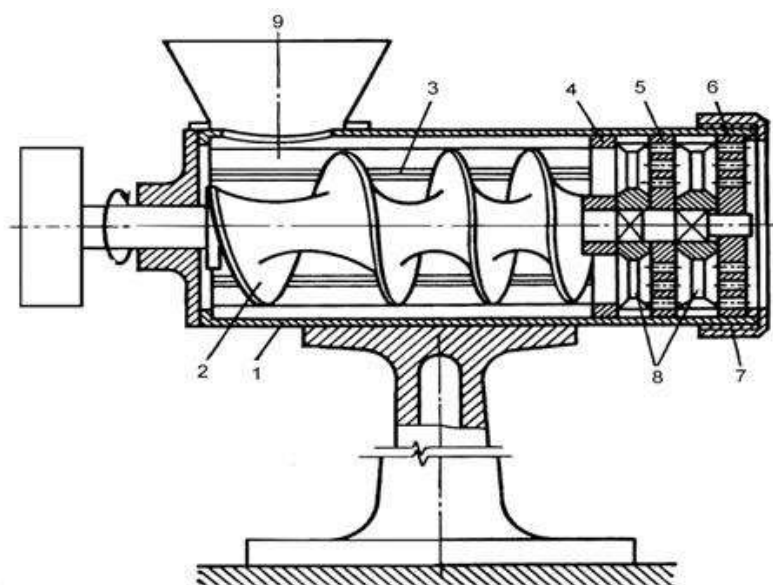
Принципова схема вовчка: 1 – робоча камера; 2 – шнек; 3 – ребра; 4 – підрізна решітка; 5,6 – ножові решітки; 7 – затяжна гайка; 8 – хрестоподібні ножі; 9 – чаша завантаження.
